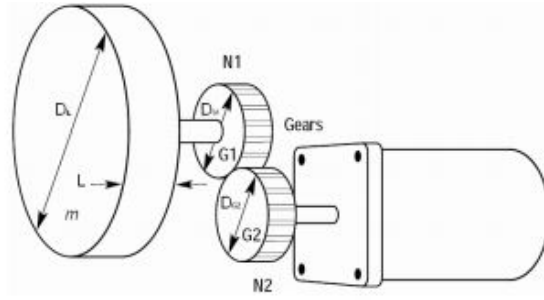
Transmissão de movimento de um motor com acoplamento de rodas dentadas [36].
